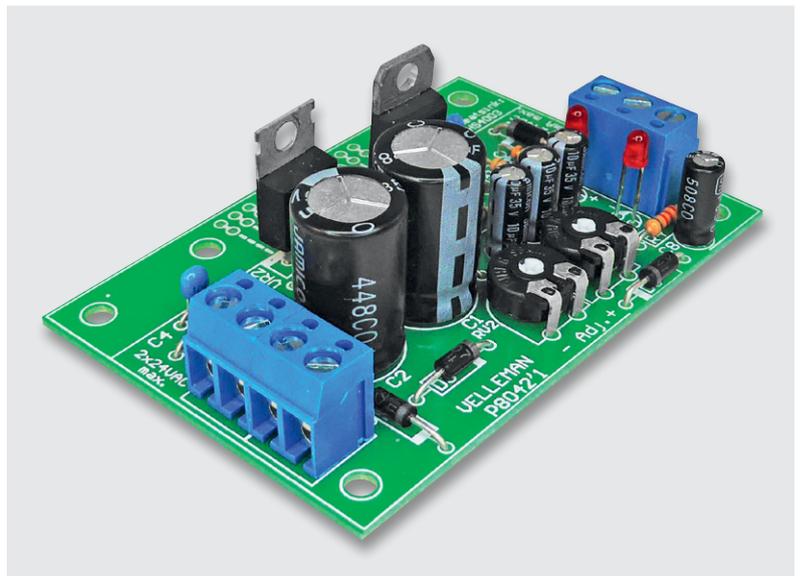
Die fertig bestückte Netzteil-Baugruppe
